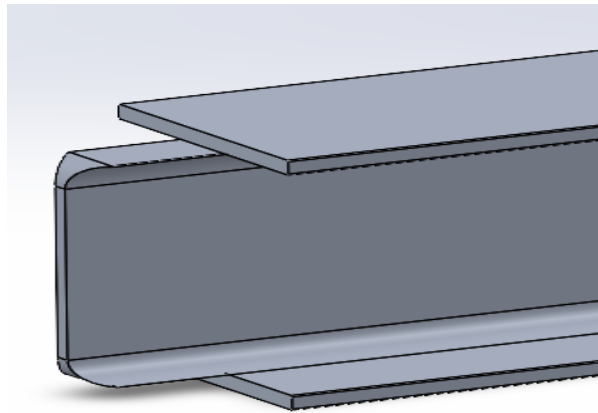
Géométrie modélisée d'une extrusion usinée 3D
